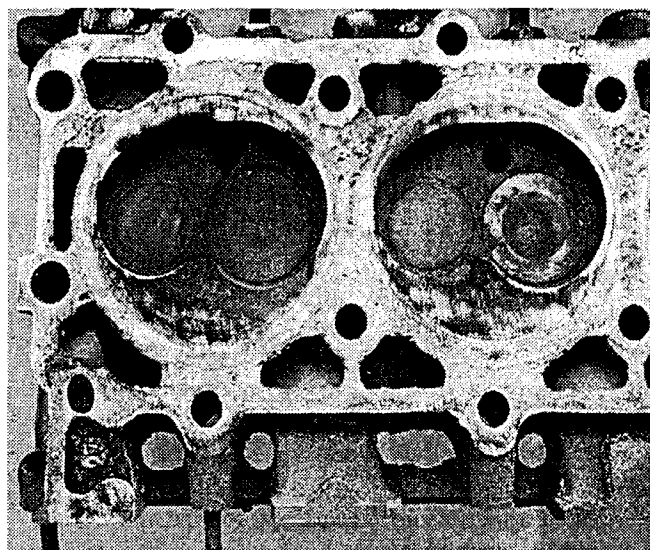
Изношенная головка блока цилиндров двигателя ЗМЗ-53
